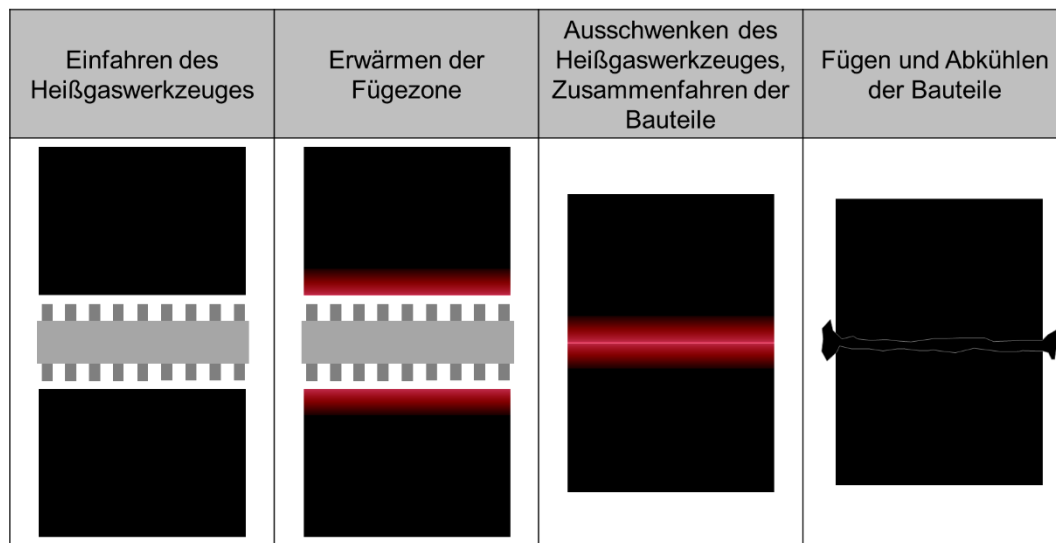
Verfahrensablauf Heißgasschweißen [13, 14]
